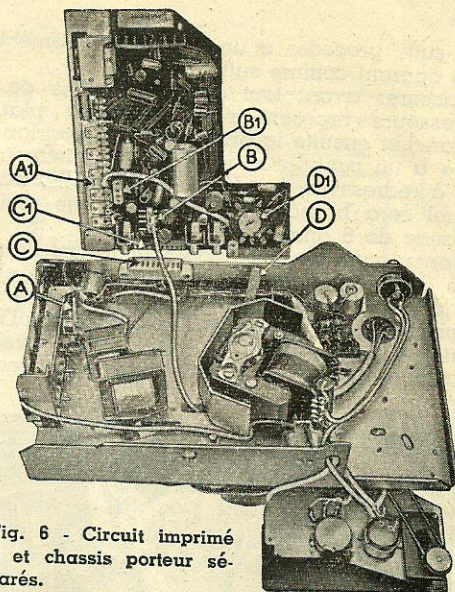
Circuit imprimé et chassis porteur séparés.
